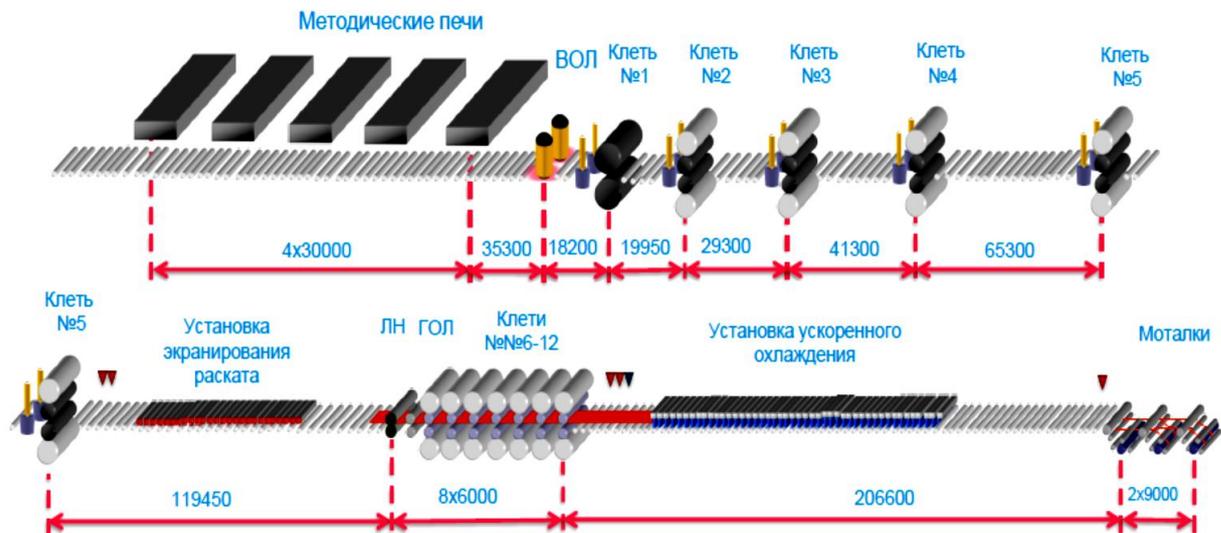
Непрерывный широкополосный стан горячей прокатки 2000 ПАО «НЛМК»: ВОЛ – вертикальный окатиноломатель; ЛН – летучие ножницы; ГОЛ – горизонтальный окатиноломатель
